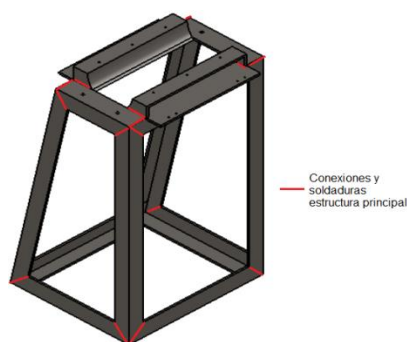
Conexiones y soldadura en la estructura principal
